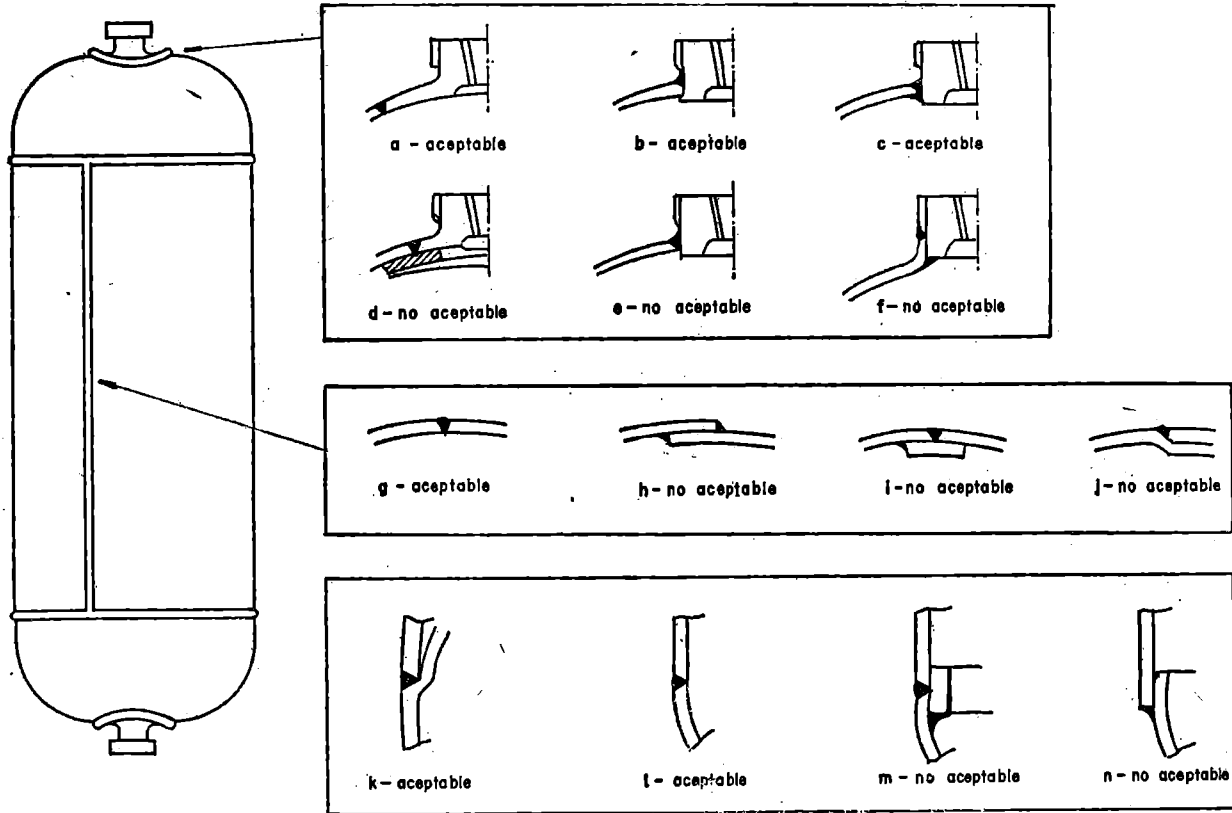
SOLDADURAS ACEPTABLES Y NO ACEPTABLES
